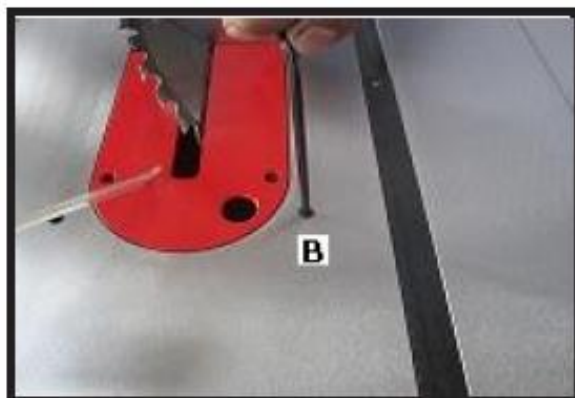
Регулировка положения под углом 45° с помощью установочного винта
